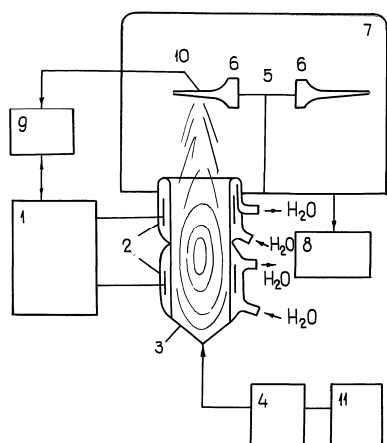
Установка ПУ-ВЧЕ для полировки и очистки: 1 – ВЧ-генератор, 2 – электроды, 3 – водоохлаждаемая РК, 4 – устройство очистки аргона, 5 – карусельное устройство, 6 – обрабатываемая деталь – лопатка газотурбинного двигателя, 7 – вакуумная камера, 8 – система откачки, 9 – система контроля-управления, 10 – термопары, 11 – система газоснабжения.
